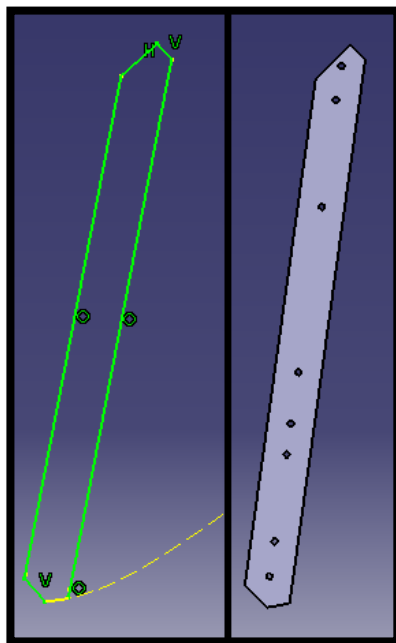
Barra diagonal 9: Primer sketch y pieza finalizada
